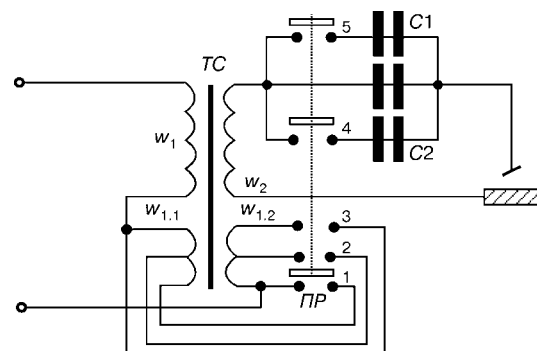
Схема РСИ с согласованной регулировкой сварочного тока
